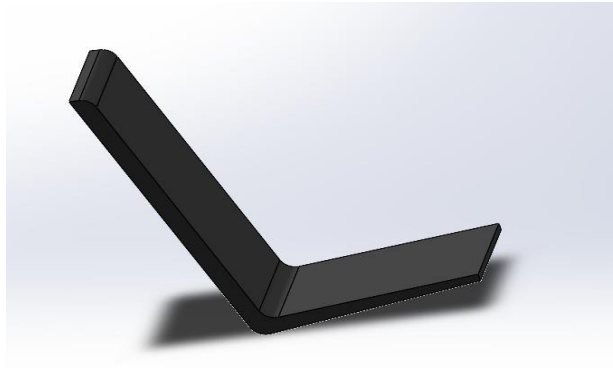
Diseño de Rampa en Mecanismo de Agarre
